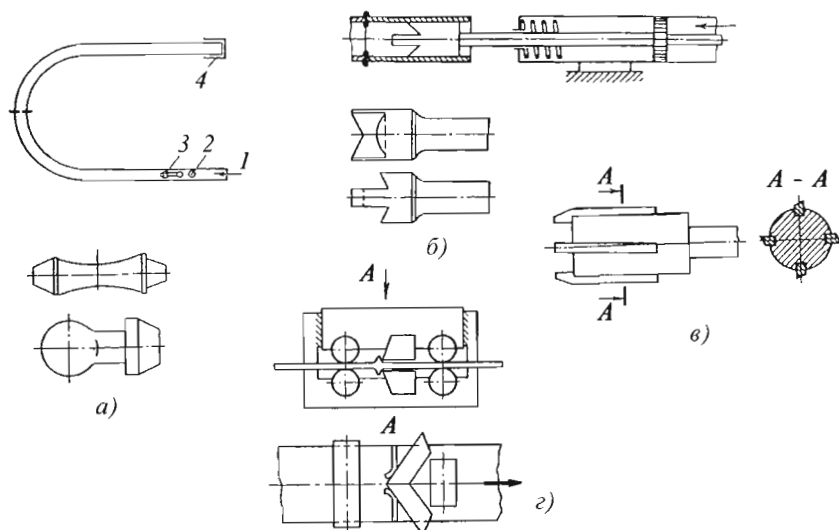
Устройство для удаления внутреннего грата при сварке труб:
